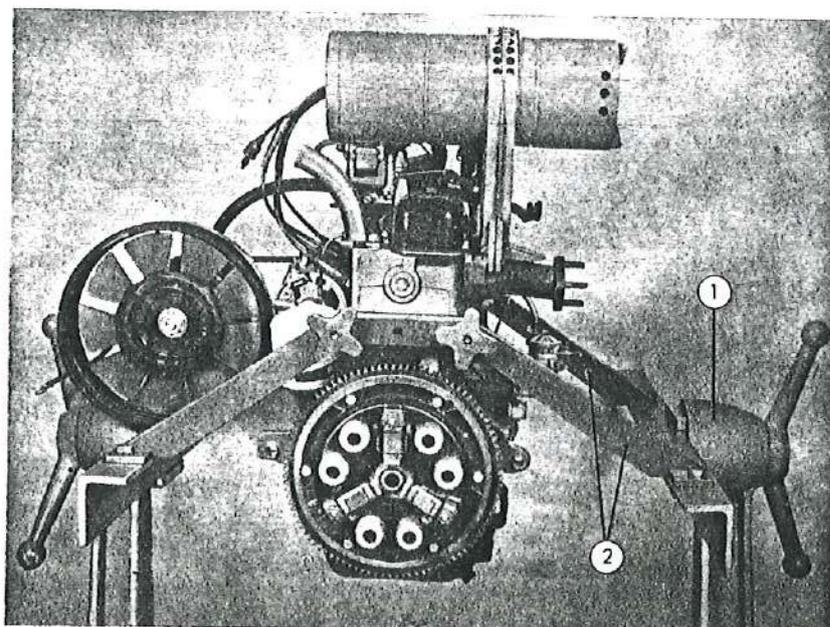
Motor sobre caballete rotativo para la revisión.
